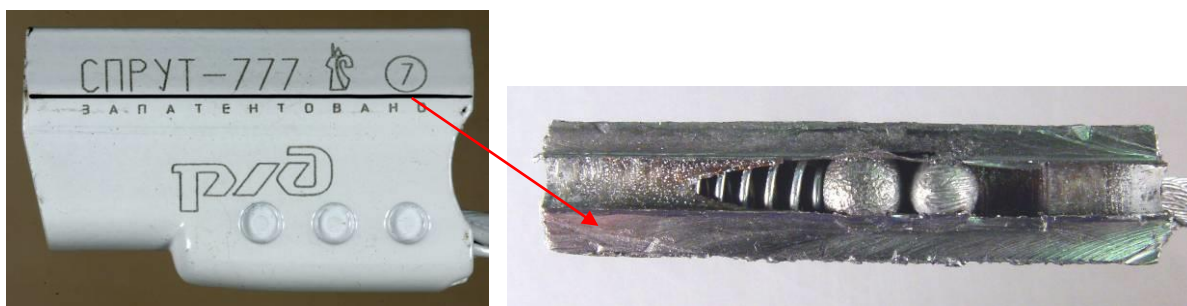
Корпус ЗПУ с разметкой разделения и часть корпуса с запирающим механизмом после распиливания
